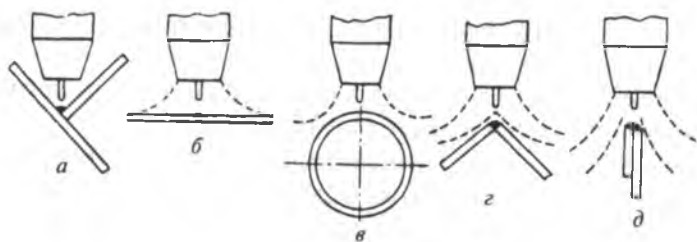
Влияние формы сварного соединения на эффективность газовой защиты
